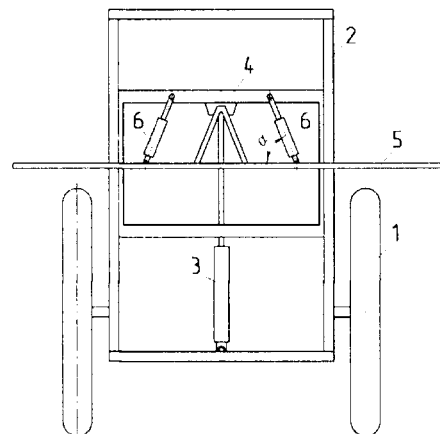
Схема к расчету амортизаторов системы стабилизации штанги: 1 — шасси опрыскивателя; 2 — рама; 3 — гидроцилиндр изменения высоты установки штанги; 4 — подвижная рамка; 5 — штанга; 6 — амортизаторы
